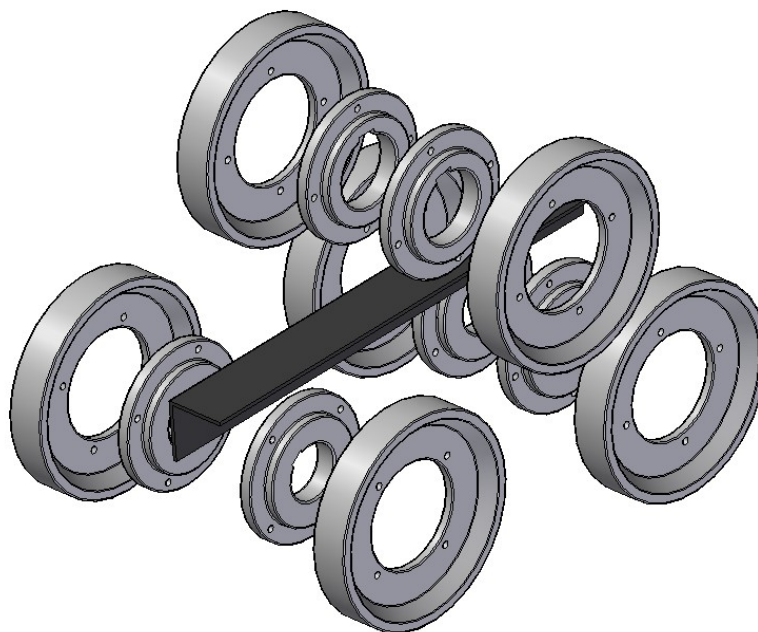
Disposición de rodillos para perfil ángulo explosionada.
